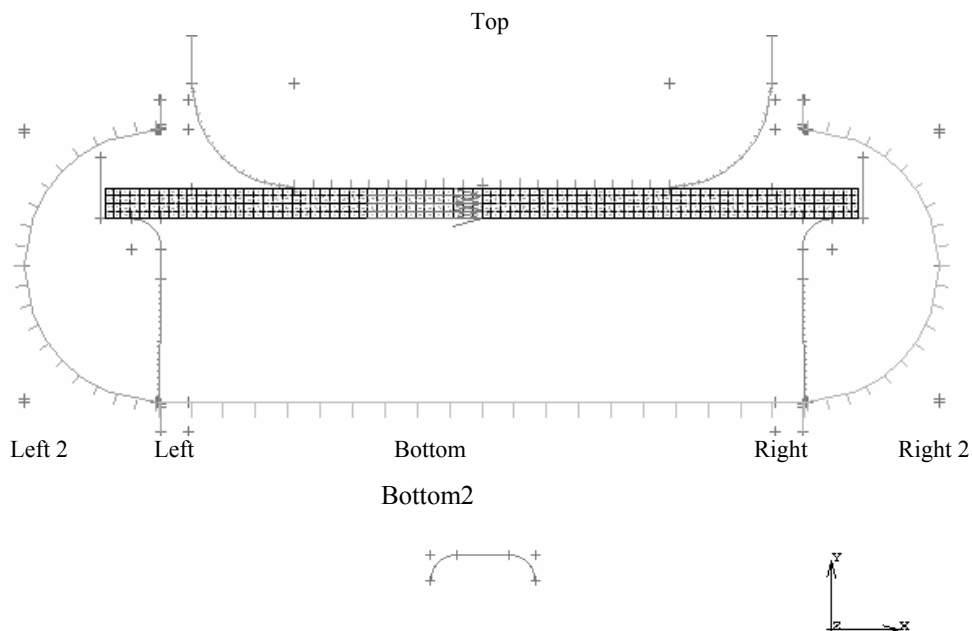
Система рабочих частей комбинированного штампа для двухугловой гибки и свертки (условно совмещены на плоскости чертежа)
